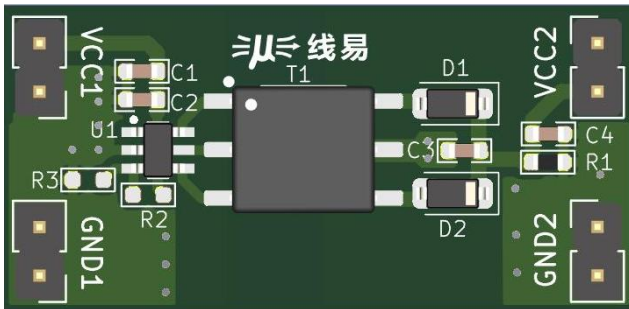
PCB 版图正面 (尺寸: 16 x 33 mm)
